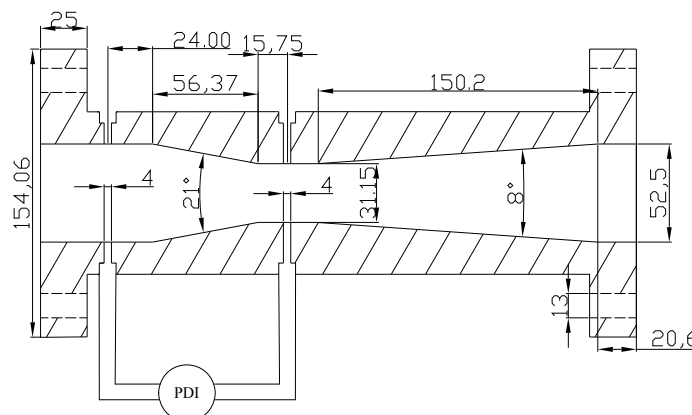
Tubo Vénturi (dimensiones en milímetros)
